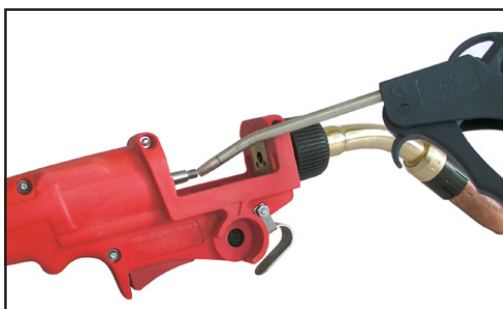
Schweißbrenner-Schlauchpaket reinigen
